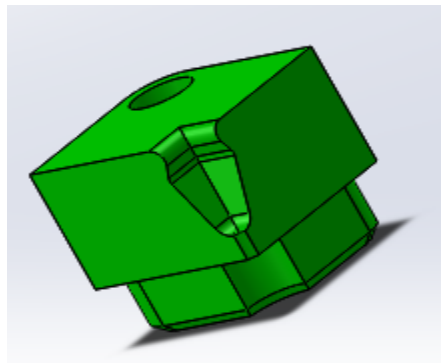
Pièce du coin réalisée par SolidWorks.
